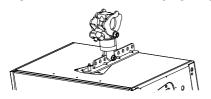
Z5147 Rota Clamp et Q Flying adapter
